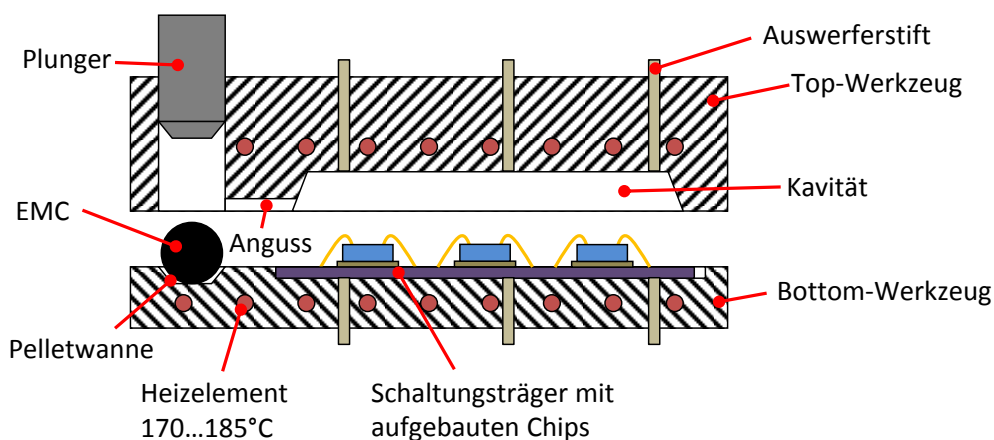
Prinzipskizze zum Transfer Molding-Werkzeug.
